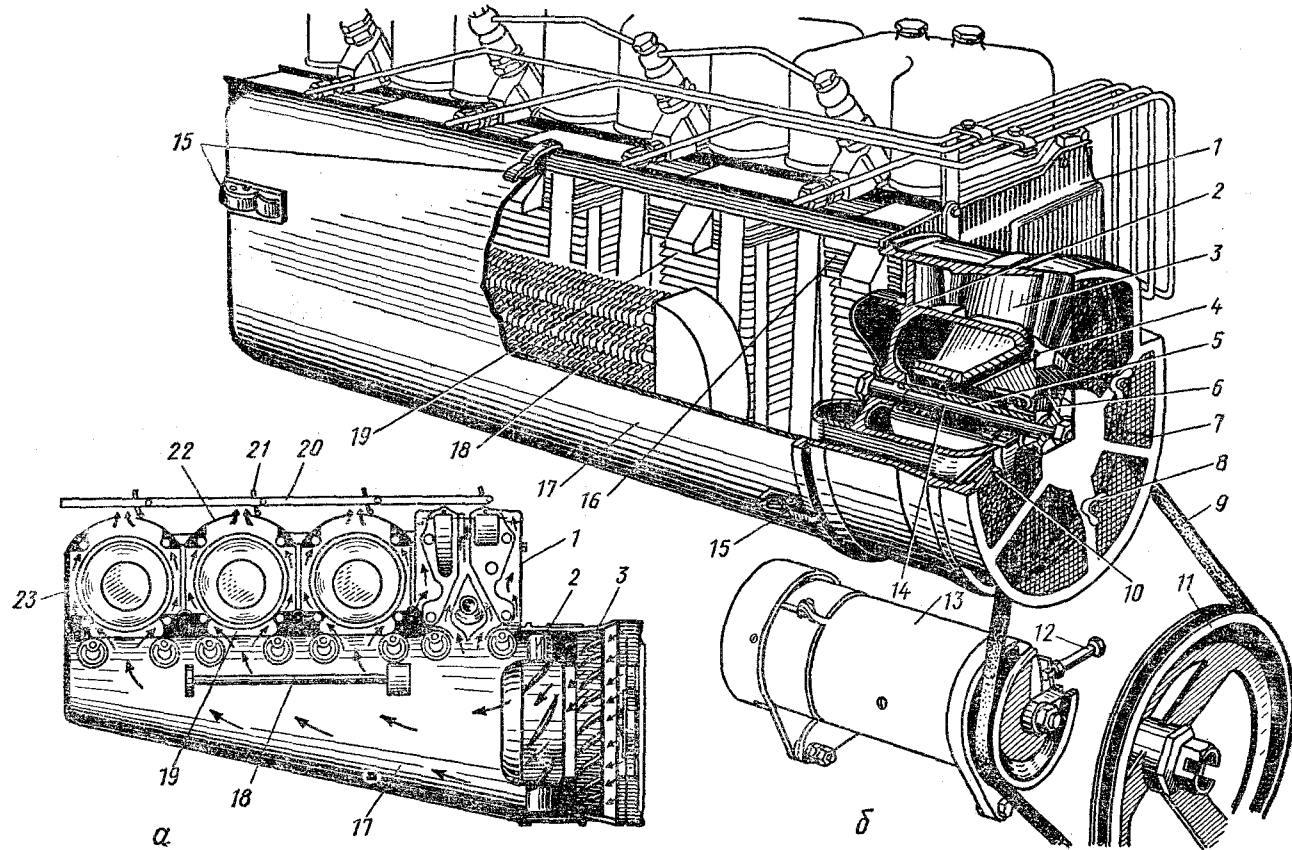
Система воздушного охлаждения (двигатель Д-37М):
